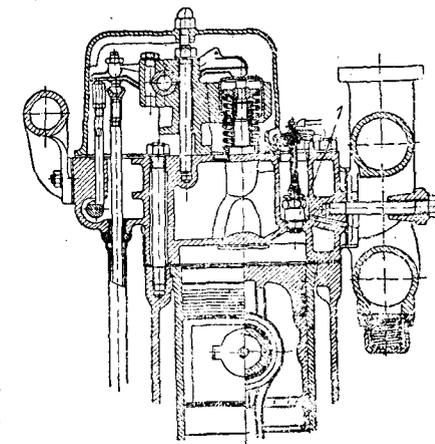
Головка и часть цилиндра двигателя МГ-17:
